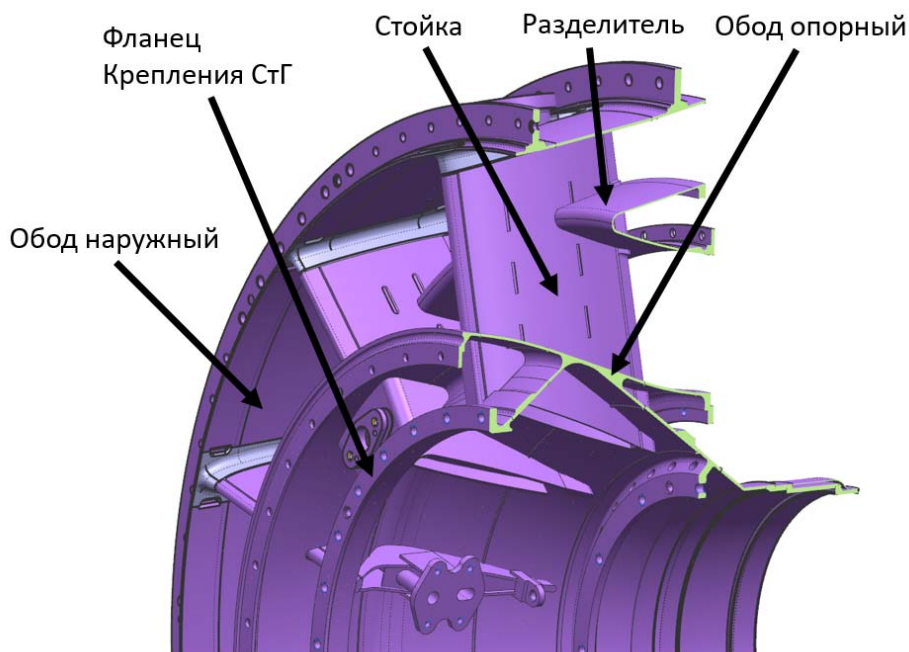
Продольный разрез конструкции промежуточного корпуса двигателя прототипа
